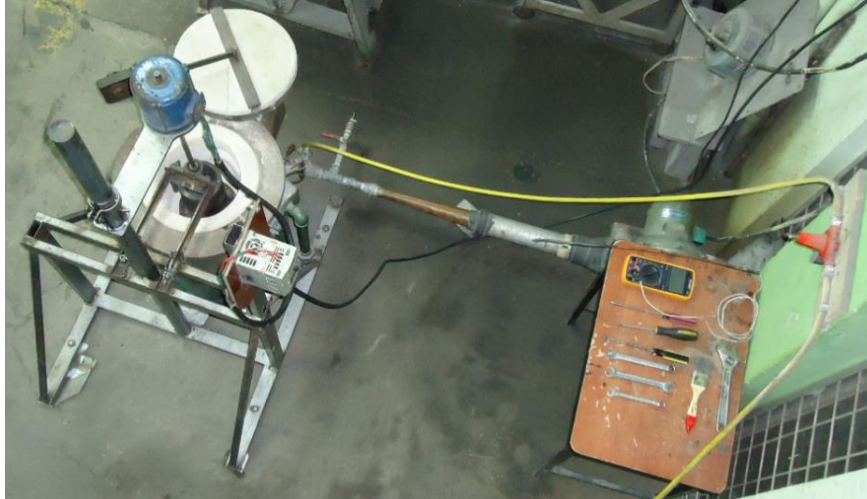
Ensamble final de partes y elementos fabricados.
